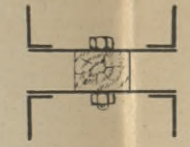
Coupe horizontale du robinet modérateur (Echelle de 0^m.05 p. m.)
